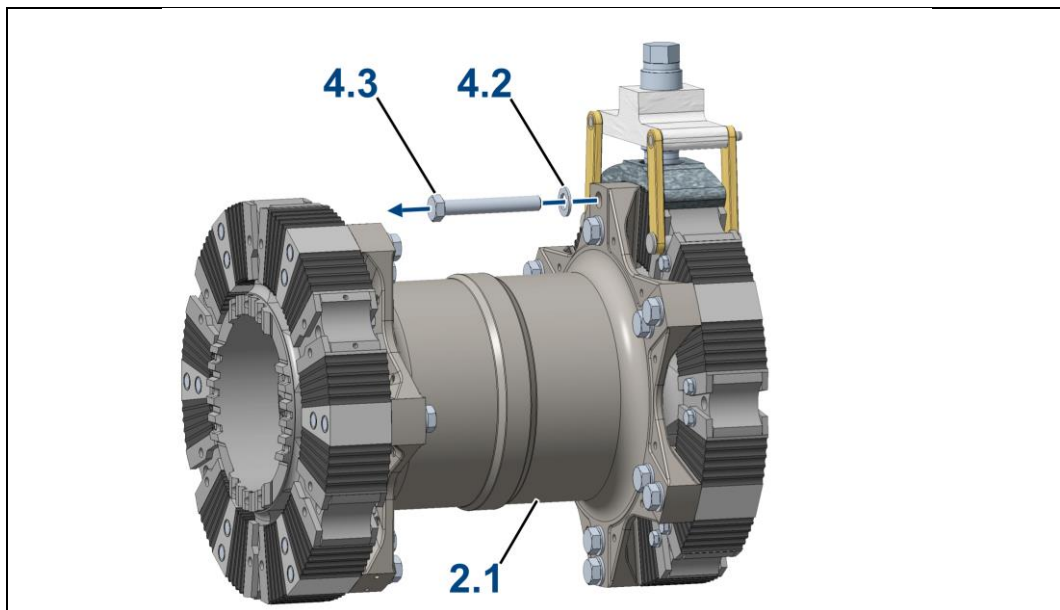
Verschraubung mit der Zwischenwelle entfernen (Beispiel) – 2.1 Zwischenwelle, 4.2 Scheibe, 4.3 Sechskantschraube
